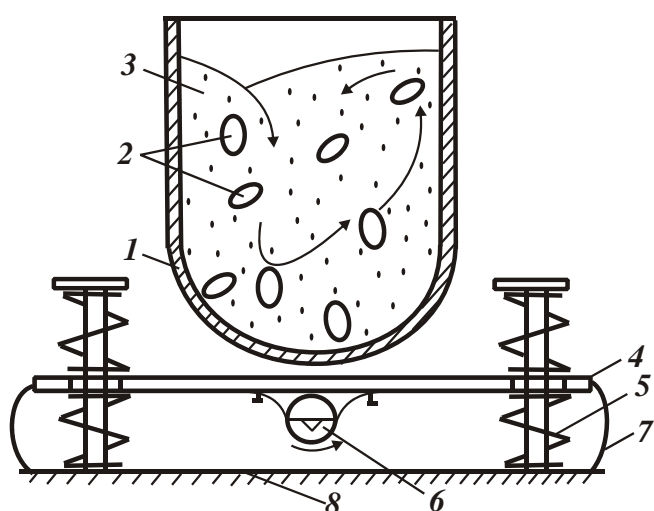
Схема виброабразивной обработки: 1 – камера; 2 – обрабатываемые детали; 3 – абразивная среда; 4 – стол; 5 – пружина; 6 – вибратор; 7 – ленточная пружина; 8 – основание.
